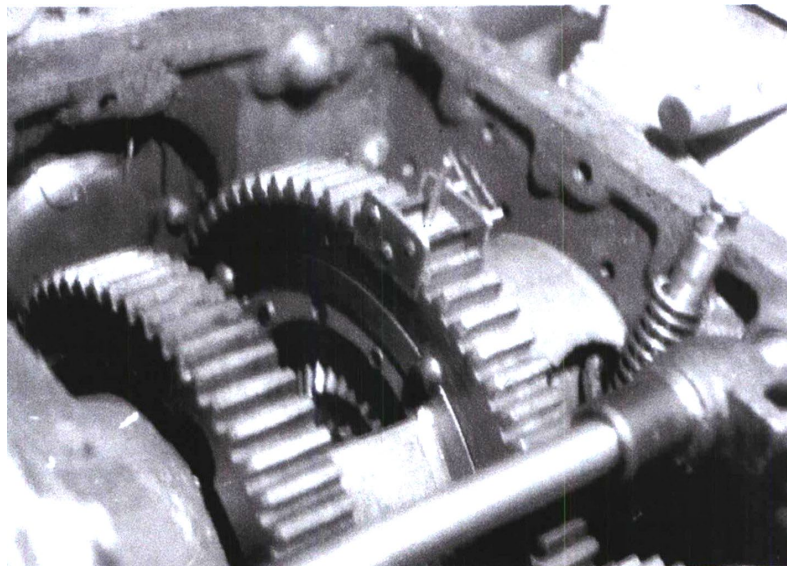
Кондуктор для зняття зліпків з поверхні зубів
